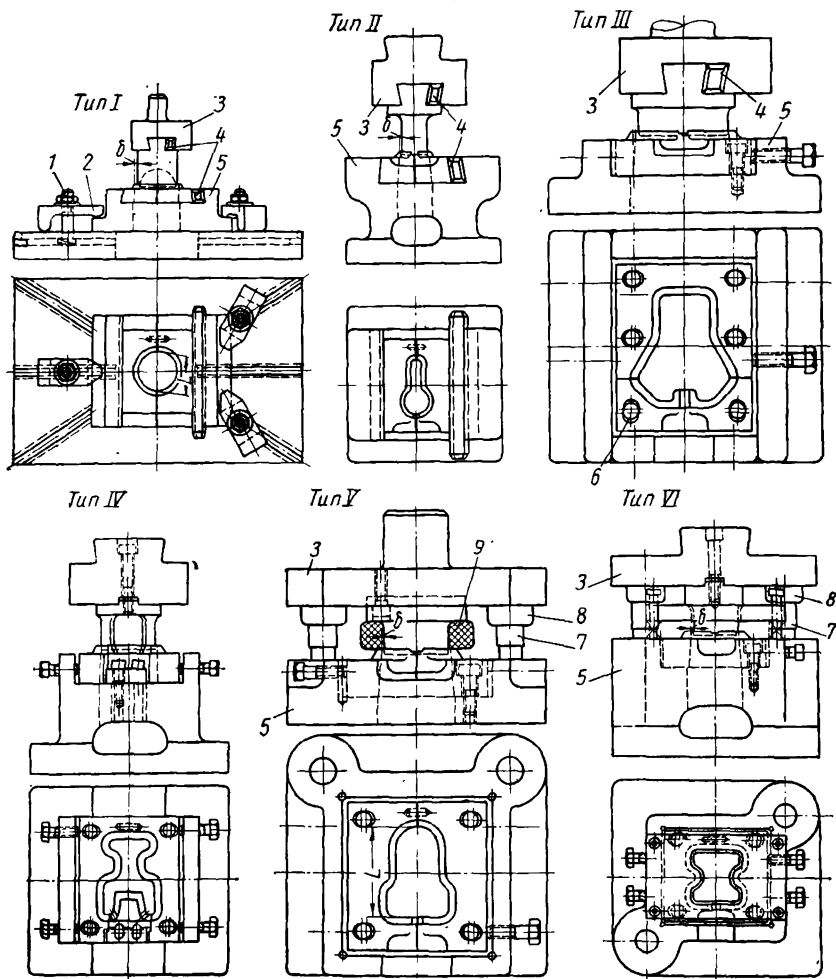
Типовые конструкции обрезных штампов: 1 — низкий штамп с креплением матрицы клином; 11 — высокий штамп с креплением матрицы клином; 111 — низкий штамп с креплением матрицы винтами; 1V — высокий штамп с креплением матрицы винтами; V — низкий штамп с направляющими колонками; VI — высокий штамп с направляющими колонками; 1 — болт; 2 — прихват; 3 — плита верхняя; 4 — клин; 5 — плита нижняя; 6 — винт; 7 — колонка; 8 — втулка; 9 — резиновый съёмник
